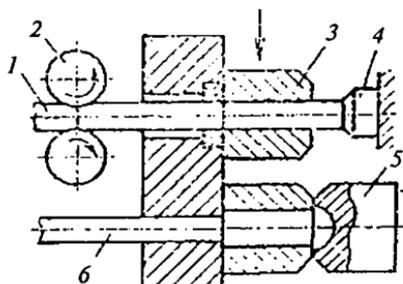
Схема штамповки на холодновысадочном одноударном автомате: 1 — пруток; 2 — ролики; 3 — матрица; 4 — упор; 5 — пуансон; 6 — толкатель
